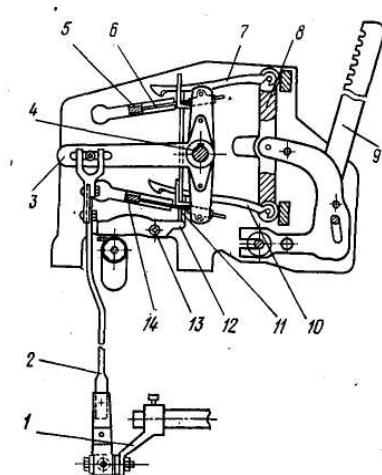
Зевообразовательная каретка РК-12 ткацкого станка АТ:
